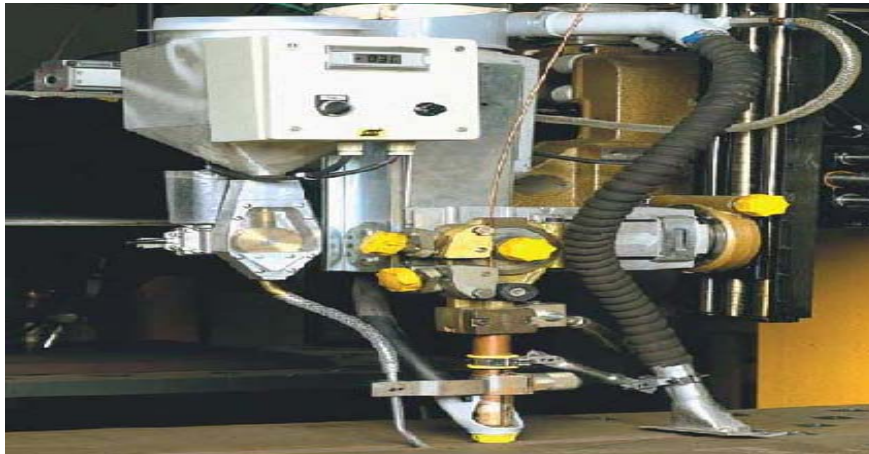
machine de soudage sous flux en poudre.
